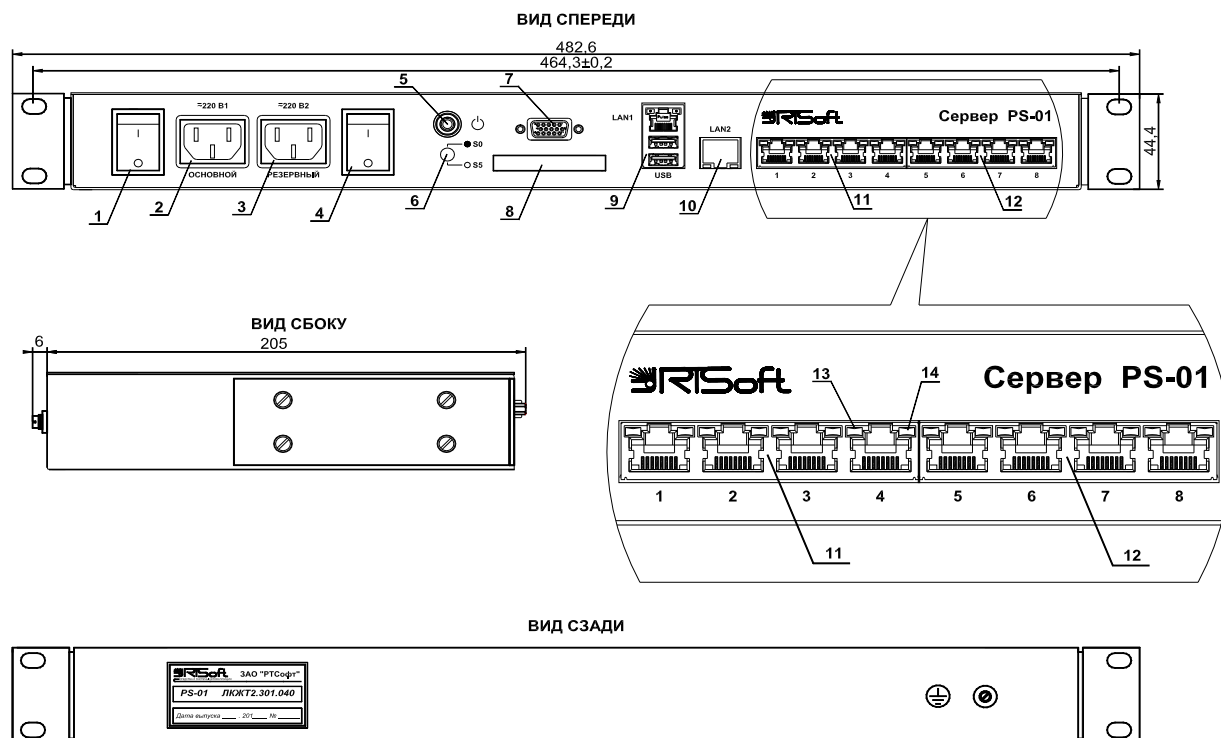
Сервер PS-01. Конструкция и установочные размеры
